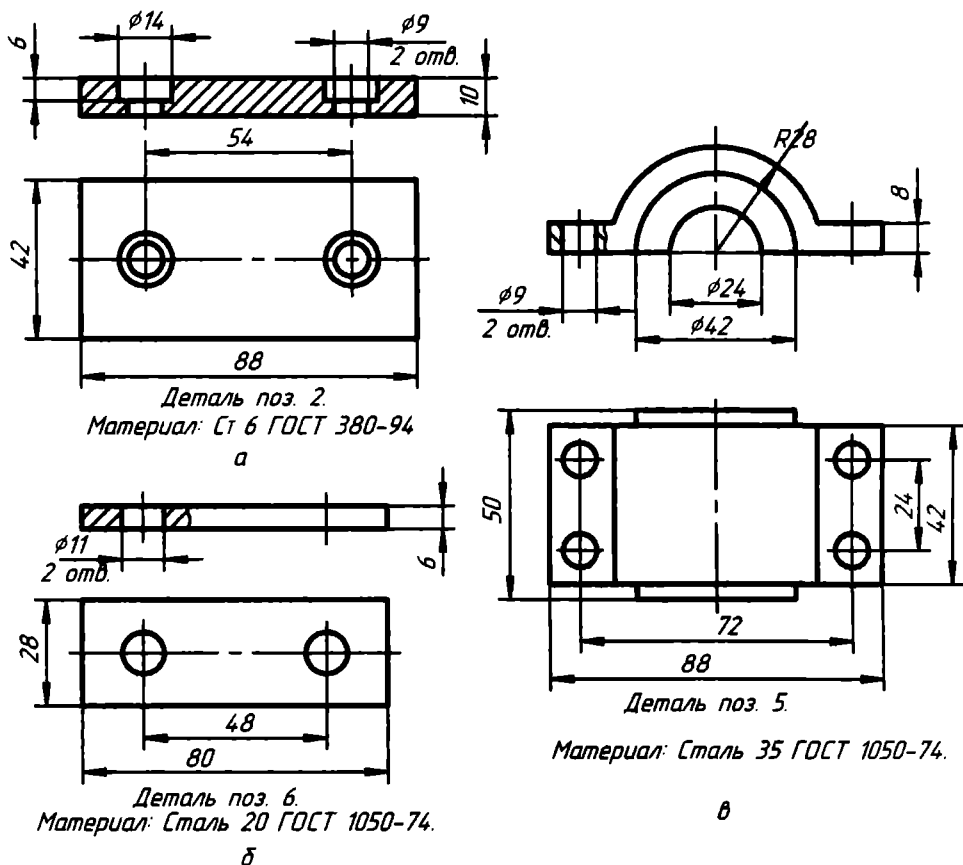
Чертежи: а — рабочей пластины; б — планки; в — крышки
